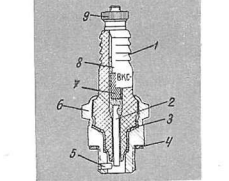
Высококальциевая свеча ВКС-32: 1 — изолятор; 2 — центральный электрод; 3 — теплозащитная втулка; 4 — уплотнительное кольцо; 5 — боковой электрод; 6 — корпус; 7 — керамическая головка; 8 — стеклогерметик СГН-11К; 9 — контактная гайка.
